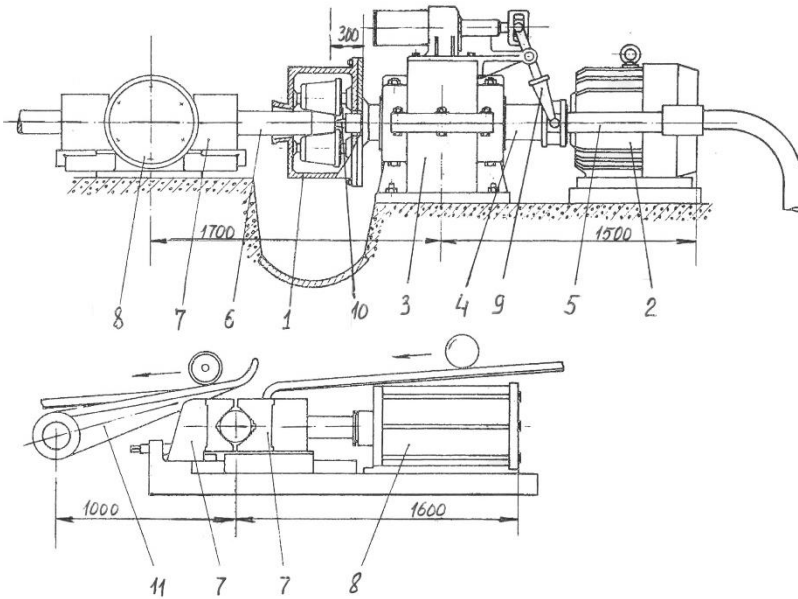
Установка для профілювання переднього кінця заготовки: 1 – роликівка касета; 2 – електропривод; 3 – редуктор; 4 – полий шпиндель; 5 – ствол зацентрувача; 6 – заготовка; 7 – затискачі; 8 – гідроциліндр; 9 – важельний механізм; 10 – бойок; 11 – лапи викидача
